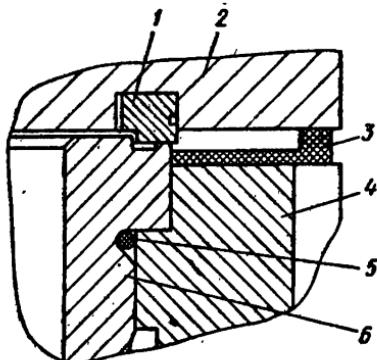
Стыки головки цилиндра и гильзы, головки и блока цилиндров:
